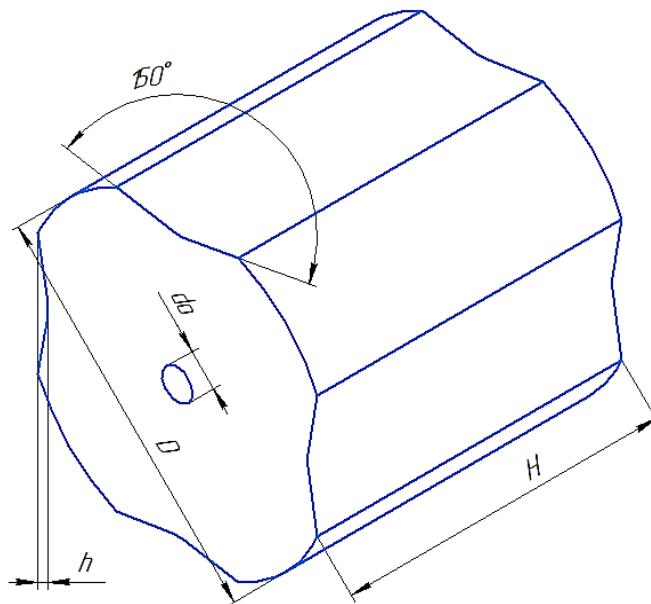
3D-модель профільованої заготовки на чотирипроменевий переріз
